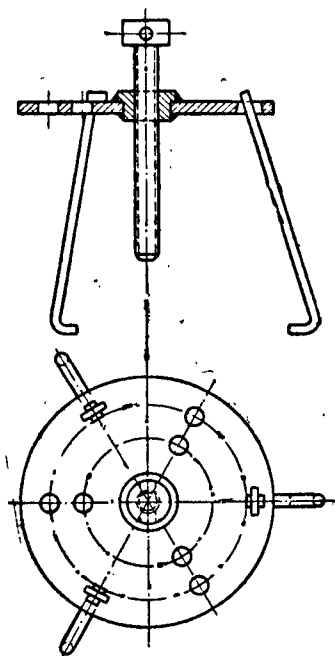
Приспособление для выпрессовки подшипникового щита мотор-генератора
